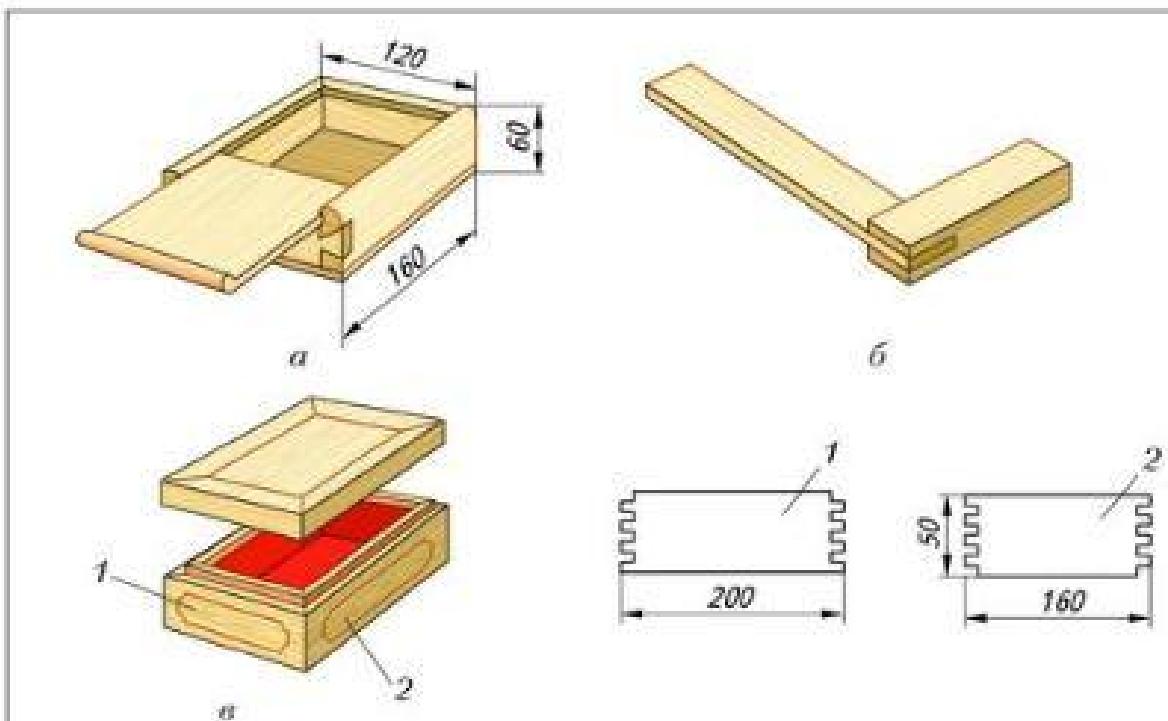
Изделия из древесины с шиповыми соединениями: *а* – коробка для мелких деталей; *б* – угольник; *в* – шкатулка: 1, 2 – боковые стенки
